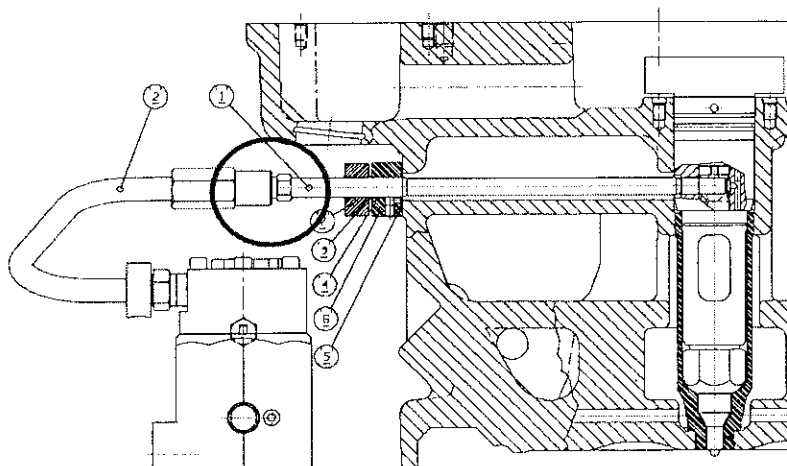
Unión modificada de la tubería principal de inyección con la pieza de conexión
